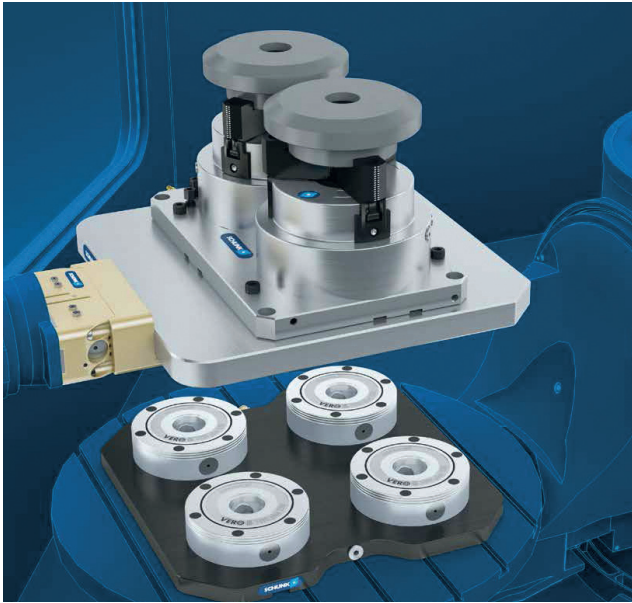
Закрепление и наладка деталей на паллетах вне станка
